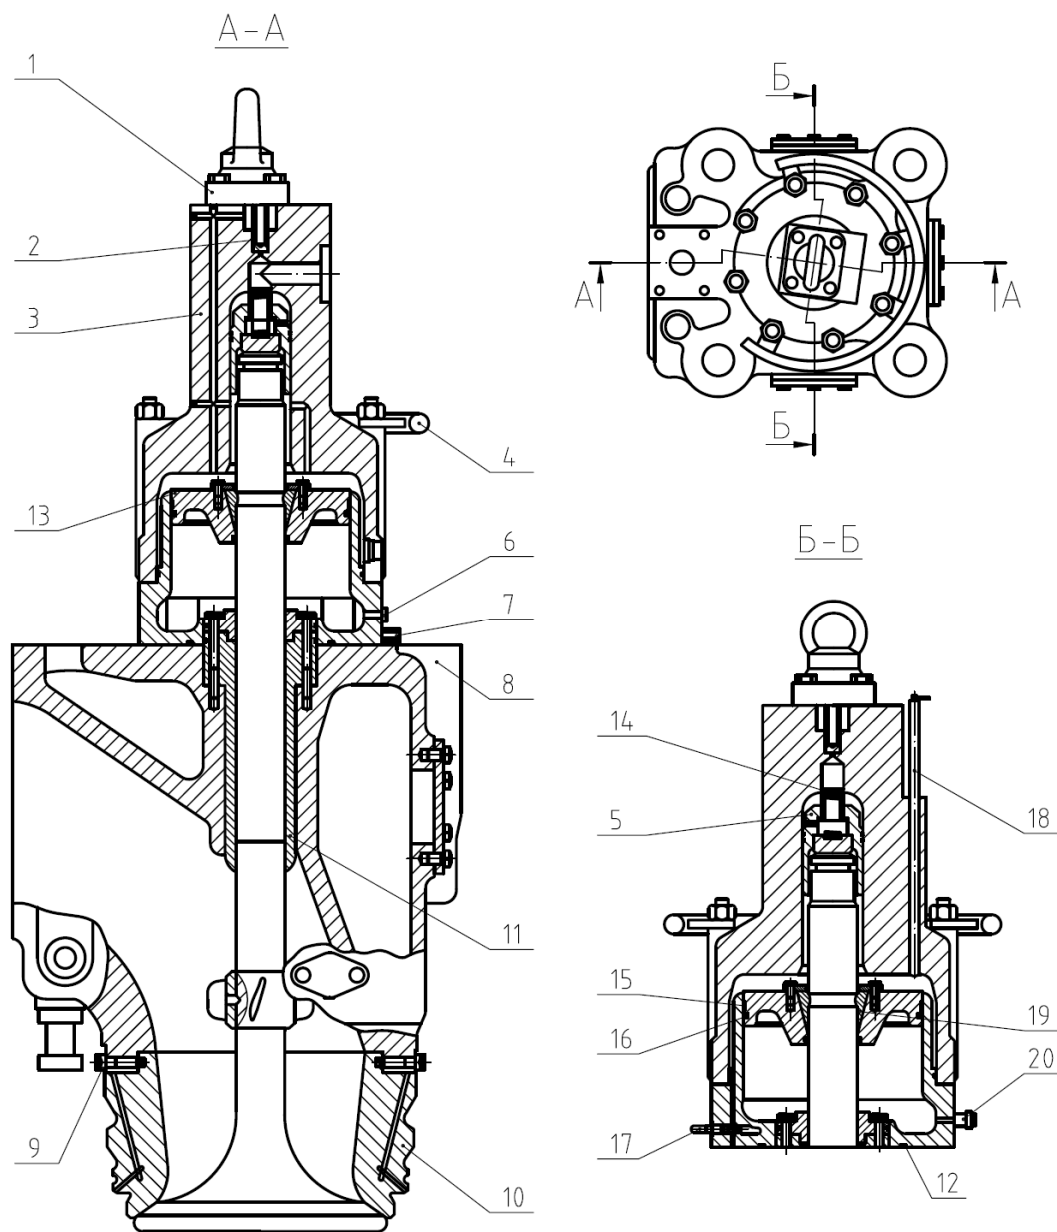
Випускний клапан: 1 – рем-болт; 2 – дросель; 3 – гідроциліндр; 4 – кільцеве огородження; 5 – гідропоршень; 6 – вентиляційна пробка; 7 – шаровий кран; 8 – корпус клапана; 9 – стопорні болти; 10 – сідло клапана; 11 – направляюча втулка; 12 – кільце ущільнююче; 13 – пневматичний поршень; 14 – демпфер поршня; 15 – тефлонове направляюче кільце; 16 – тефлоне ущільнююче кільце; 17 – запобіжний клапан; 18 – гідравлічна труба високого тиску; 19 – сухарі; 20 – управляючий блок
